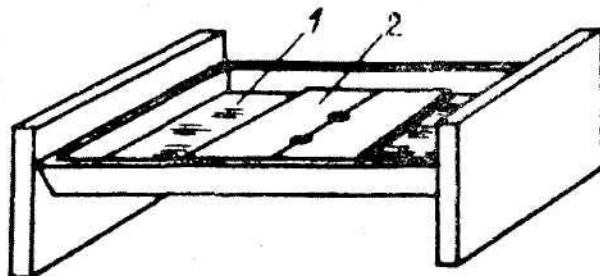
Приспособление для сварки проб из чугунных пластин: 1— вода для охлаждения проб; 2 — собранная проба
